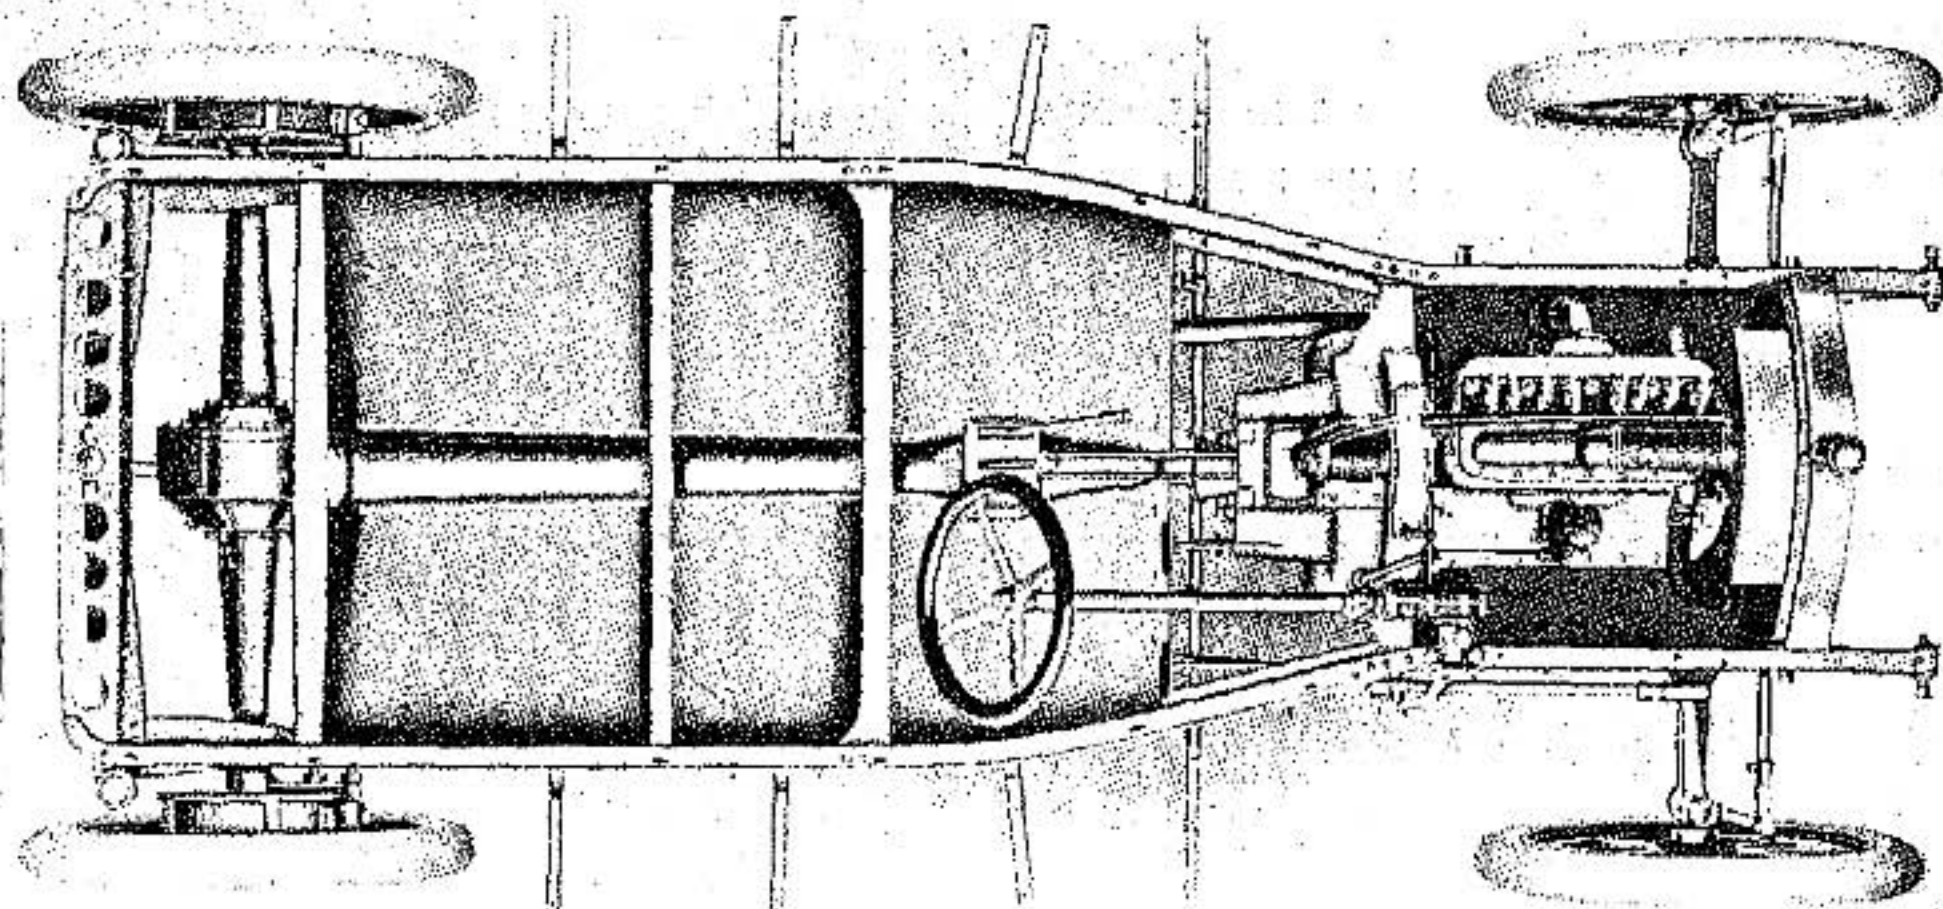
Шасси Гупмобиль 17 HP видъ сверху.
